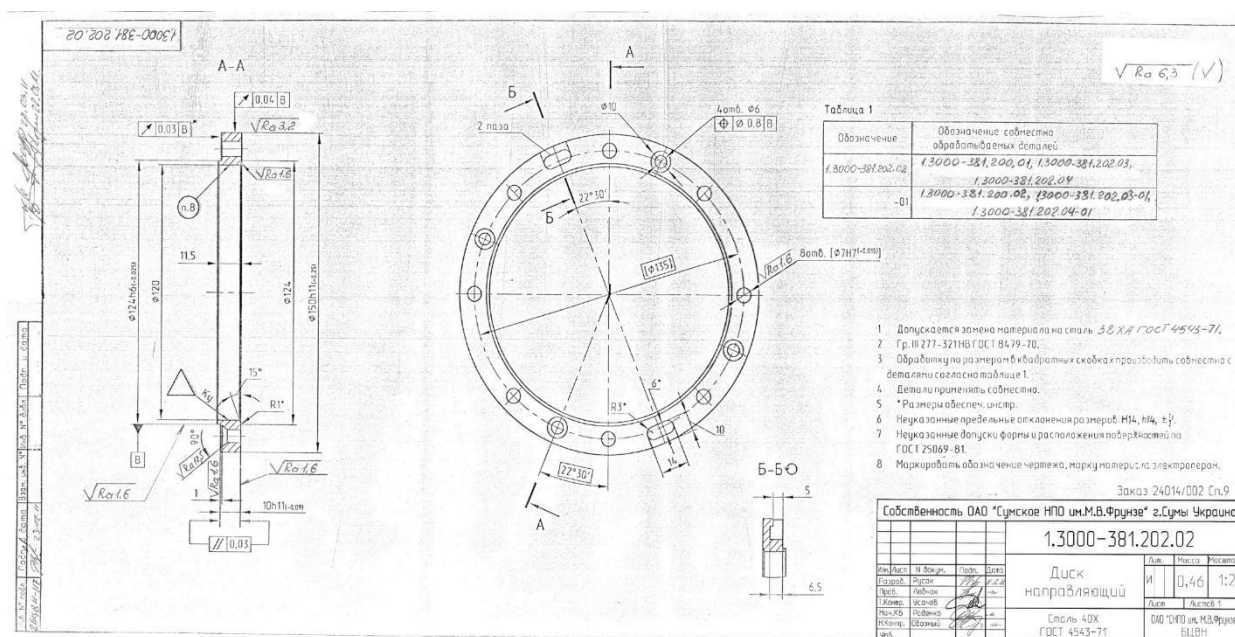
Креслення деталі «Диск направляющий»
